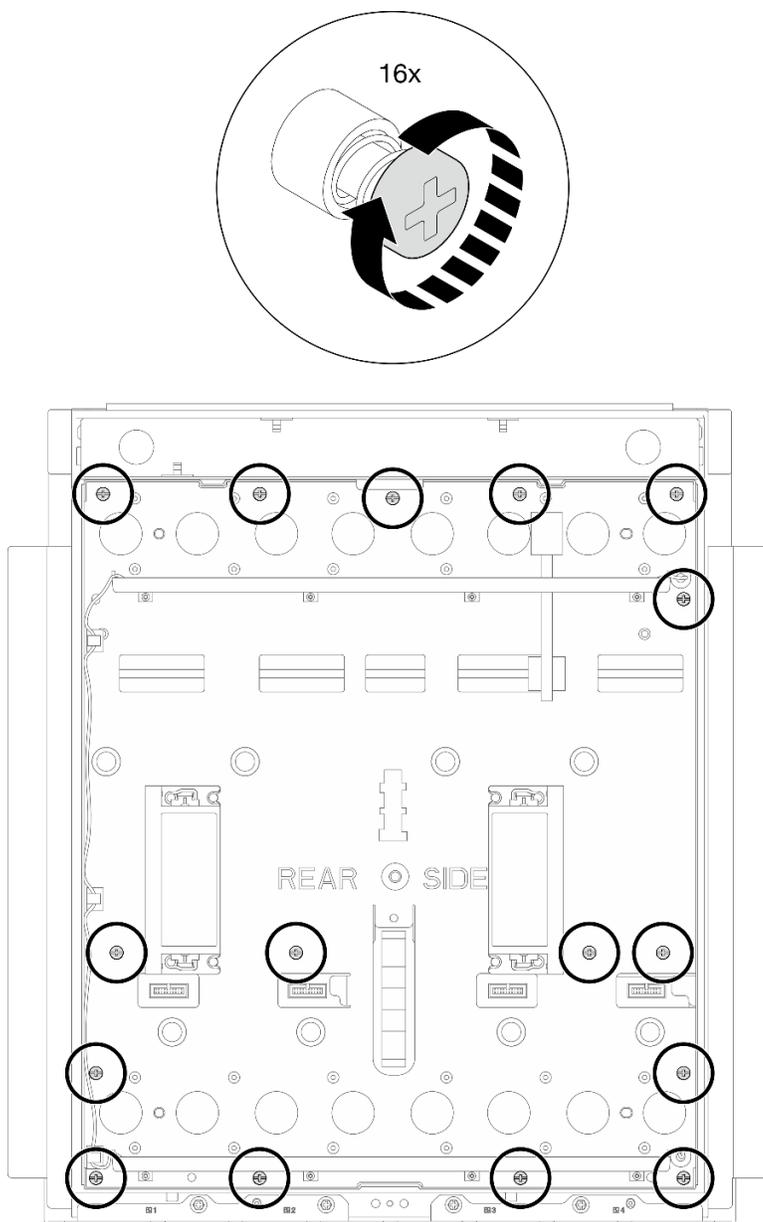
Fixation des vis imperdables sur l'assemblage de la plaque médiane
